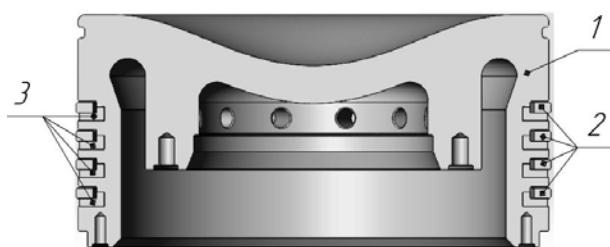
Сборка головки поршня судового МОД типа L35MC: 1 – головка поршня; 2 – поршневые кольца; 3 – протвоизносные кольца
